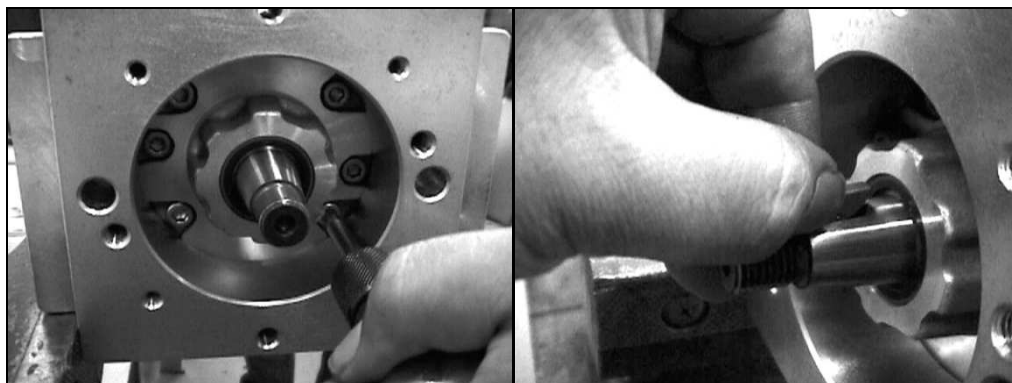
Desmontaje del cuerpo de la bomba, pernos y chaveta.
